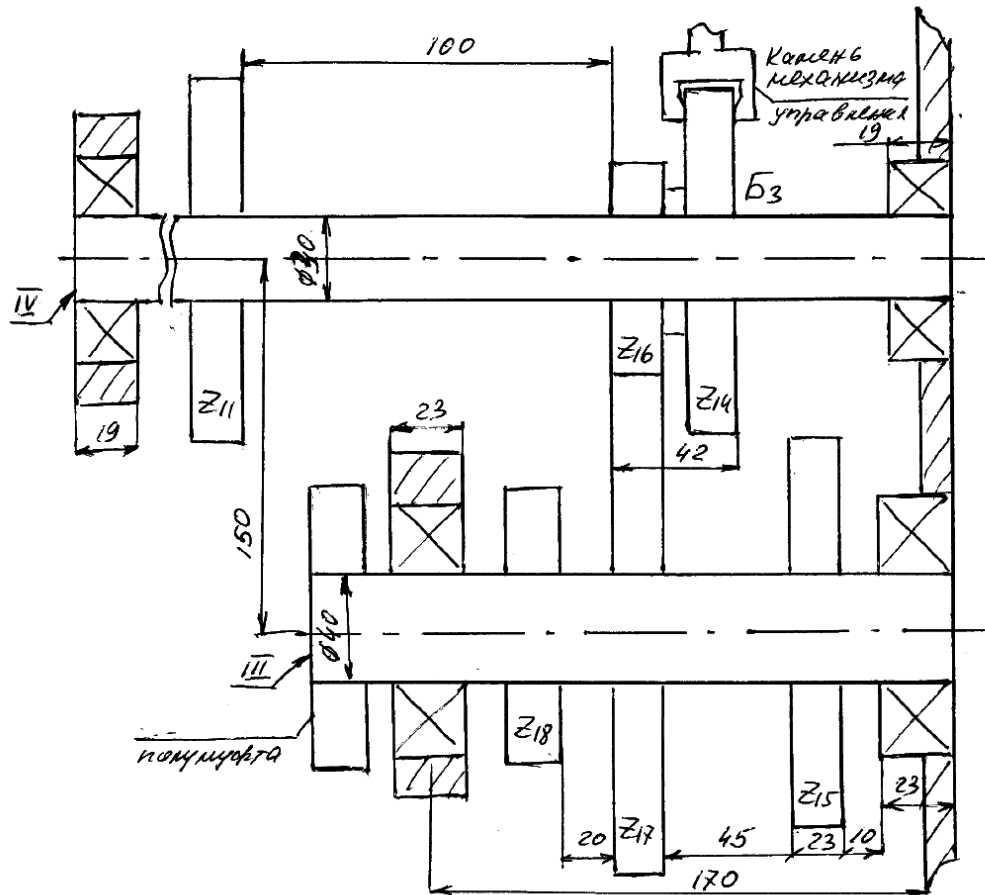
Компоновочная схема развертки наиболее нагруженной группы передач
